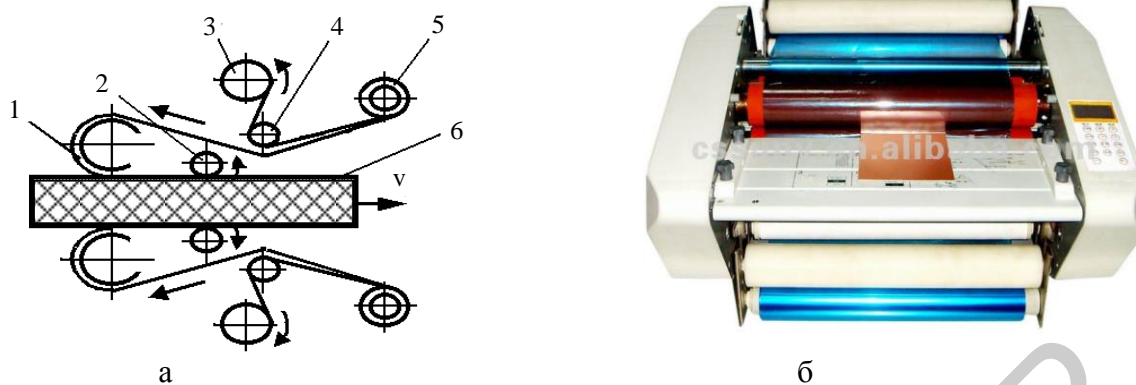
Схема (а) и внешний вид (б) ламинатора
